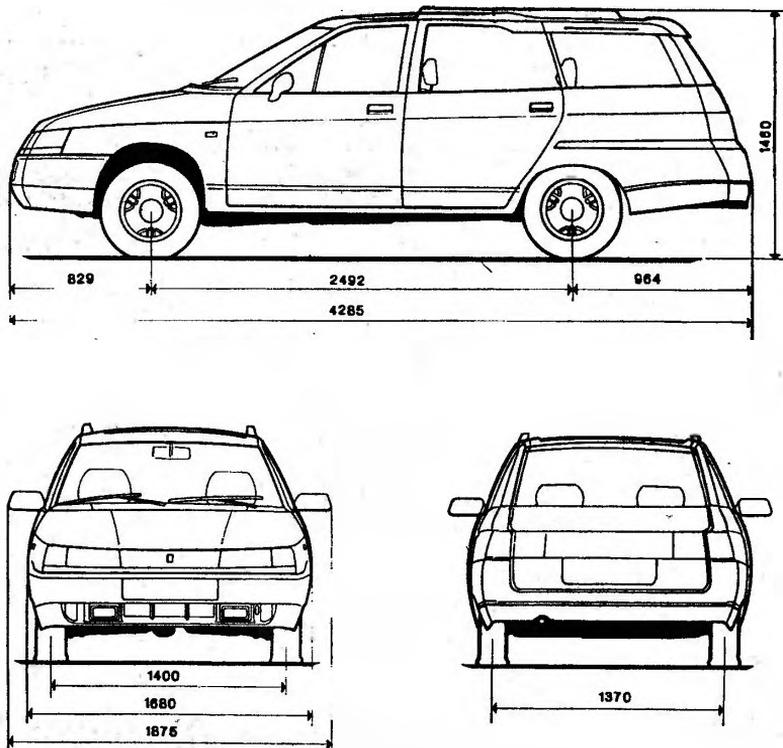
Габаритные размеры автомобиля ВАЗ-2111
